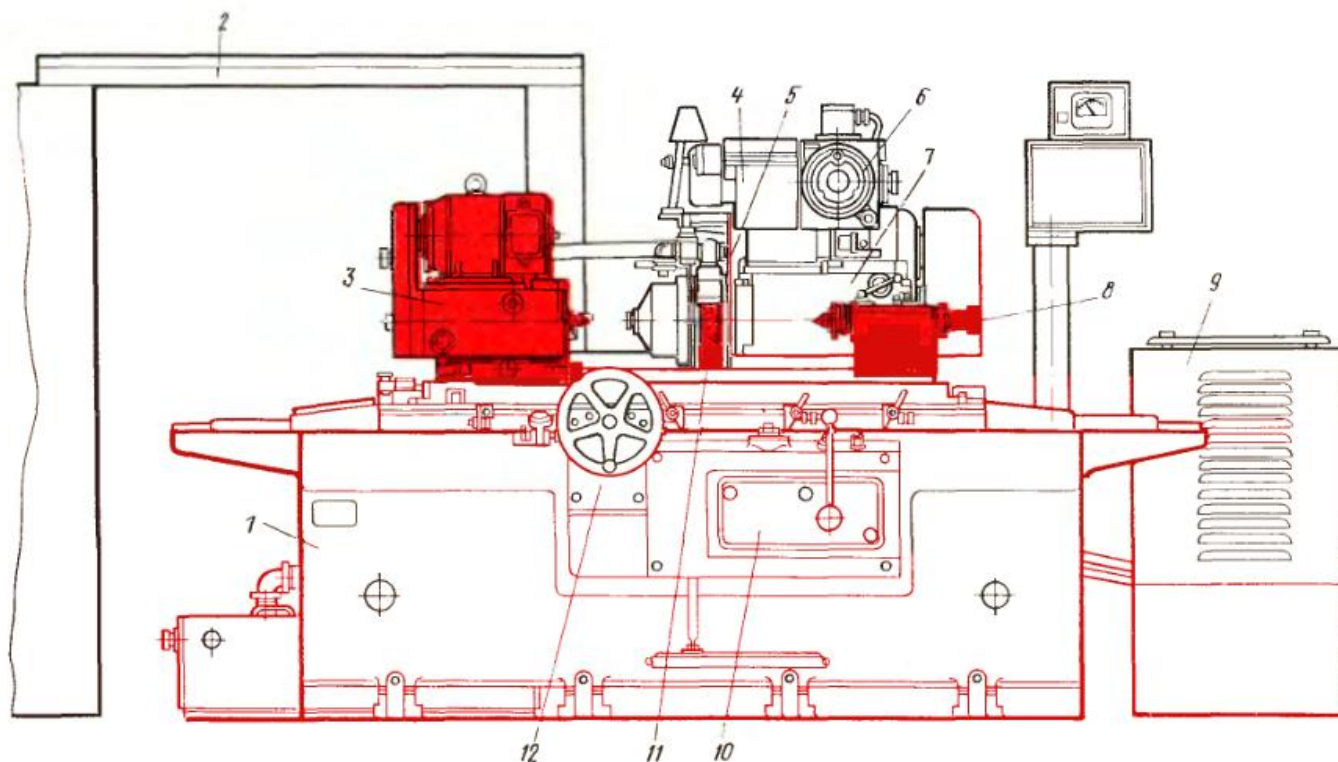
Общий вид универсального круглошлифовального станка мод. ЗУ131:
